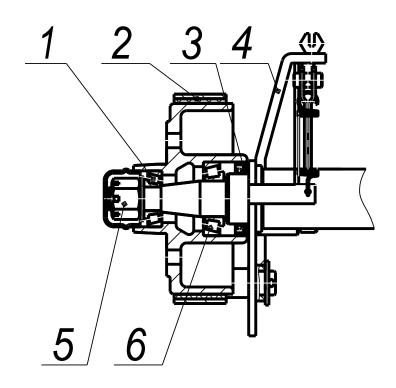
Ось с тормозом в сборе 1 — подшипник 7204; 2 — лента тормозная; 3 — манжета; 4 — рычаг; 5— гайка; 6 — подшипник 7506 НУ
